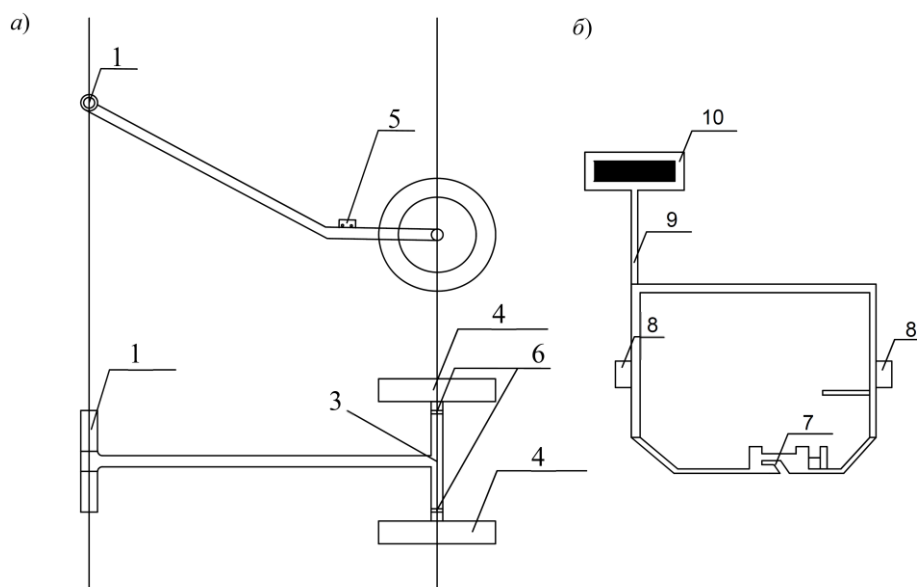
Модернизированная пожарная мотопомпа МП-800/80, а - схема предлагаемого быстросъемного шасси; б - схема модернизированной рамы. 1 – ручка; 2 – соединительная штанга; 3 – колесная ось; 4 – колесо; 5 – фиксатор; 6 – фиксатор-ограничитель; 7 - паз для установки шасси; 8 – ручки для переноски; 9 – складная штанга; 10 – фонарь.
